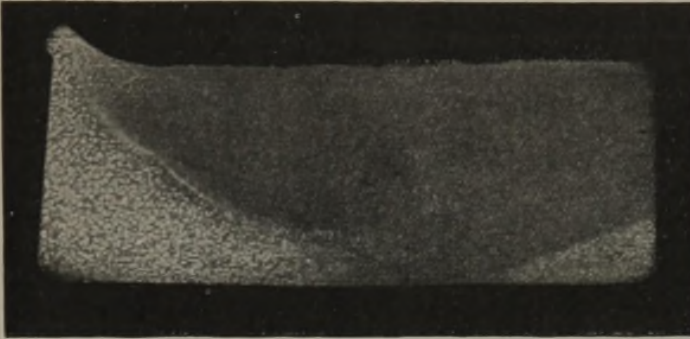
Die Verbindung zwischen Gußstück und Schweiß ist einwandfrei.
